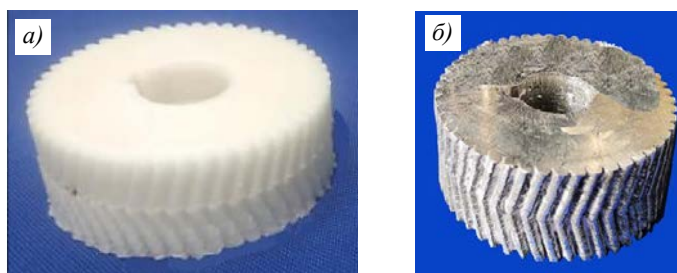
Модель, изготовленная методом послойного наплавления (FDM) (а), и отливка зубчатого колеса, изготовленная с ее использованием (б) [15]
